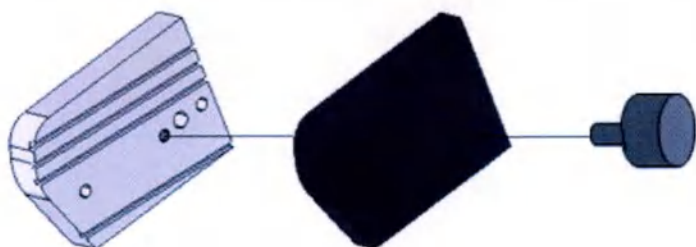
Установка опор для ультразвукового датчика СА430/СА431
